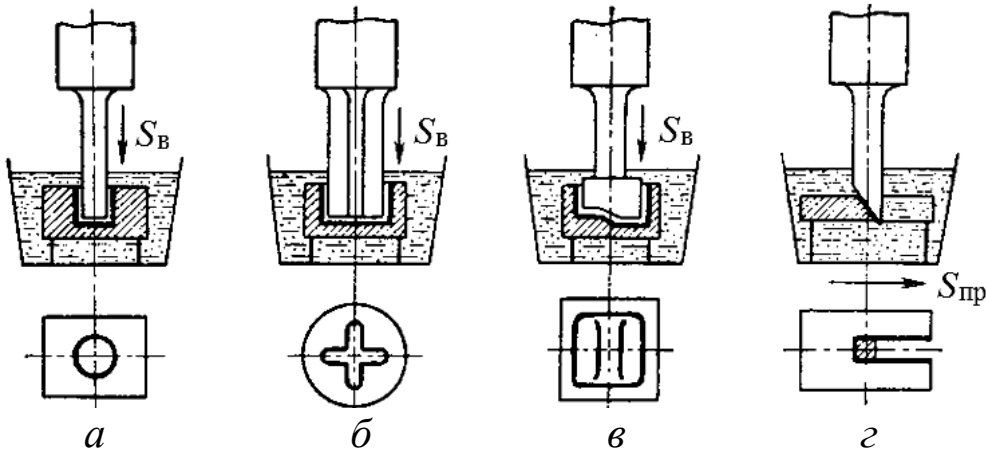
Схемы ультразвуковой обработки поверхностей заготовок
